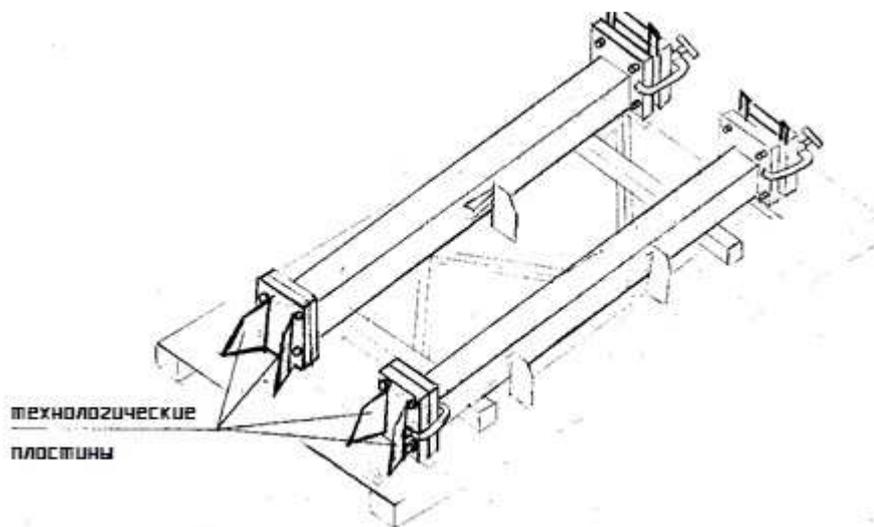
Установка и прихватка к стенду вторых фланцев
